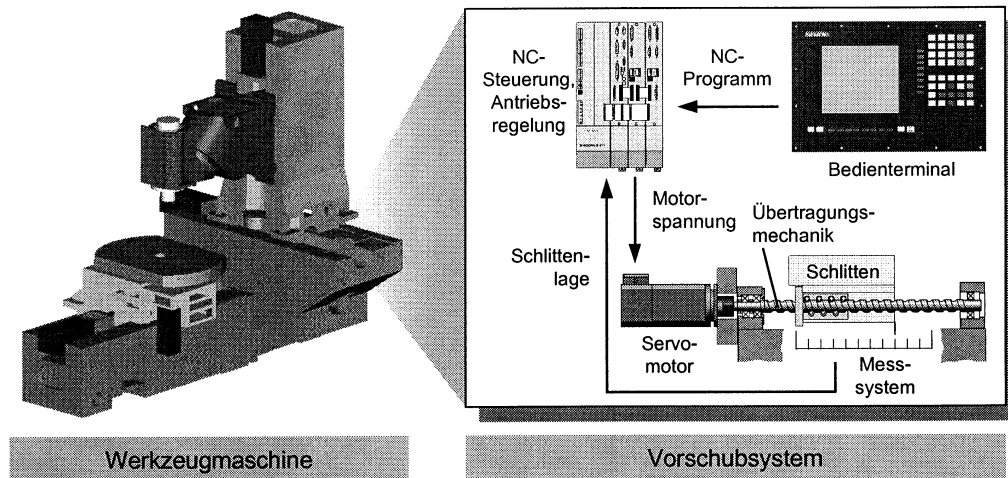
Mechatronisches System: Mechanik, Steuerungstechnik, Informationstechnik
